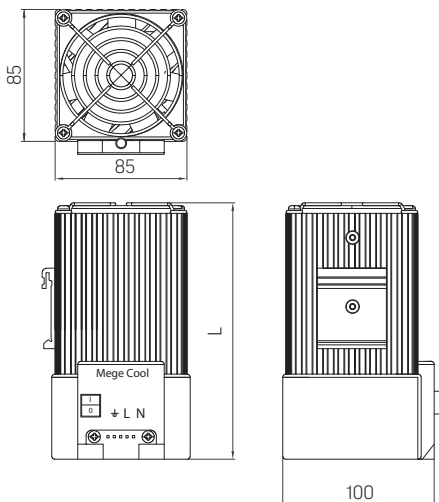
Габаритные и присоединительные размеры нагревателей MHP мощностью 250 и 400 Вт с креплением на DIN-рейку.
